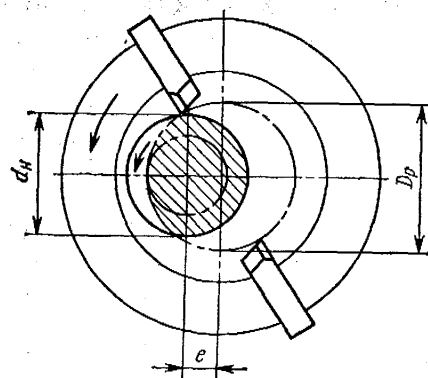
Схема вихревого нарезания наружной резьбы
